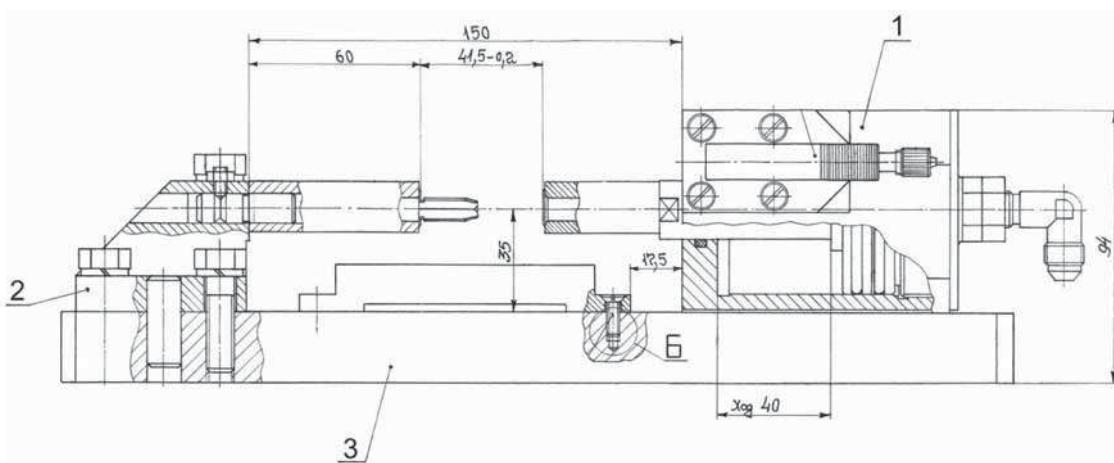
Общий вид установки для барьерного обжатия модели УБО-50
